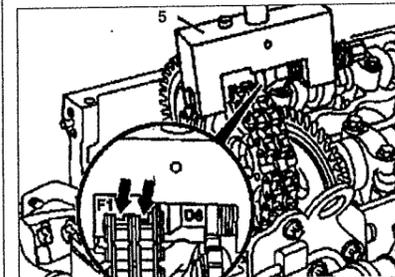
з. Установите заклепочный инструмент 5 так, чтобы направляющая уперлась (стрелка).
